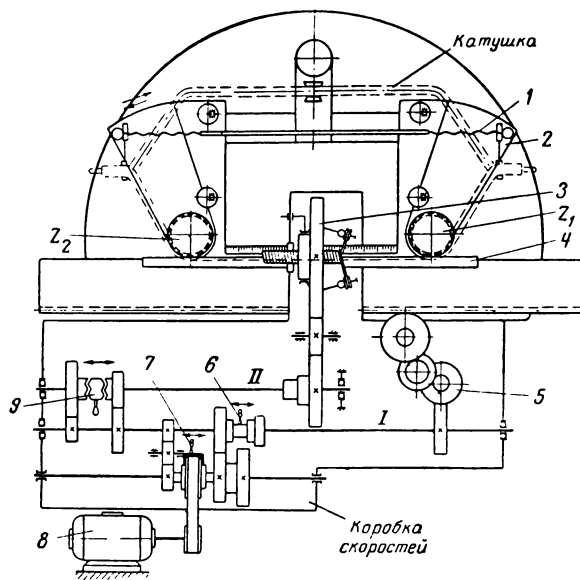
Кинематическая схема изолировочного станка ЛШ-4.
